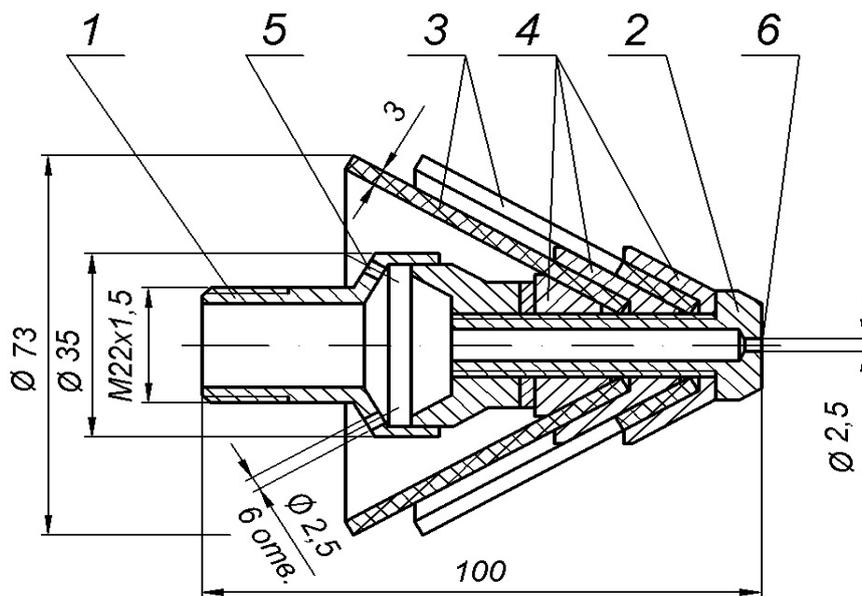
Конструкция насадки промывочной мягкой НПМ-80:
